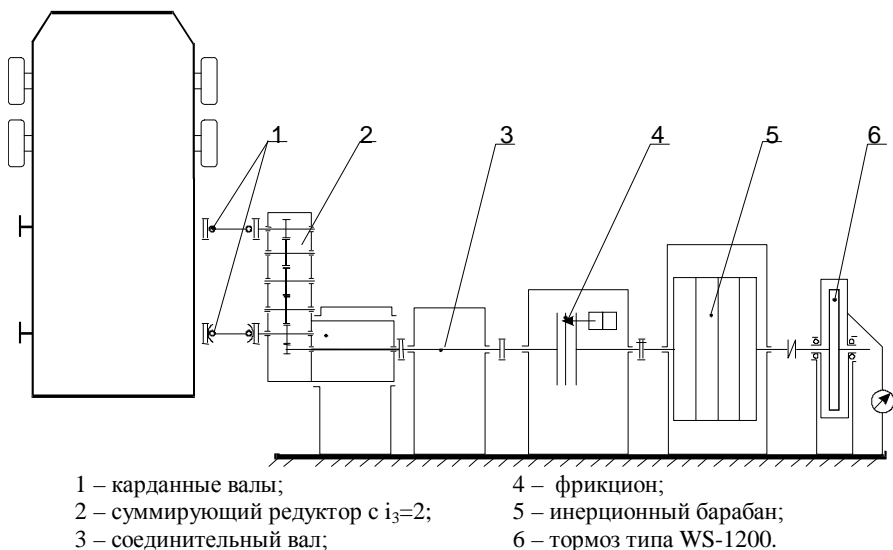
Схема сборки нагружающего устройства для испытаний колёсных БТР (на один борт)
